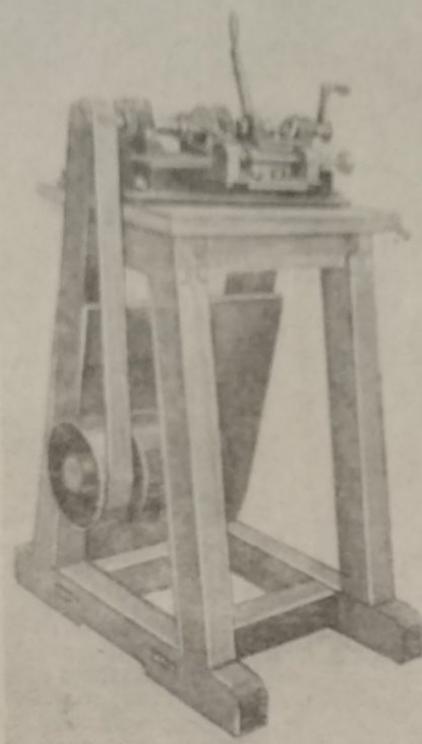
Токарно-фрезерный станок для обработки мелочи
